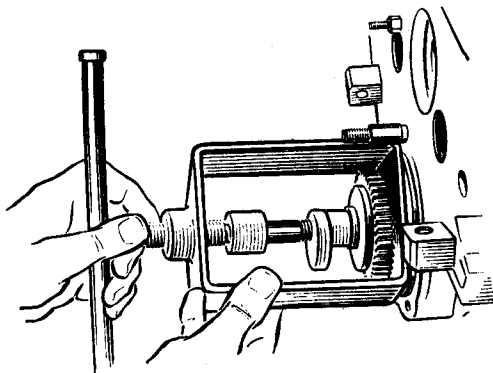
Снятие ведущей шестерни регулятора частоты вращения
